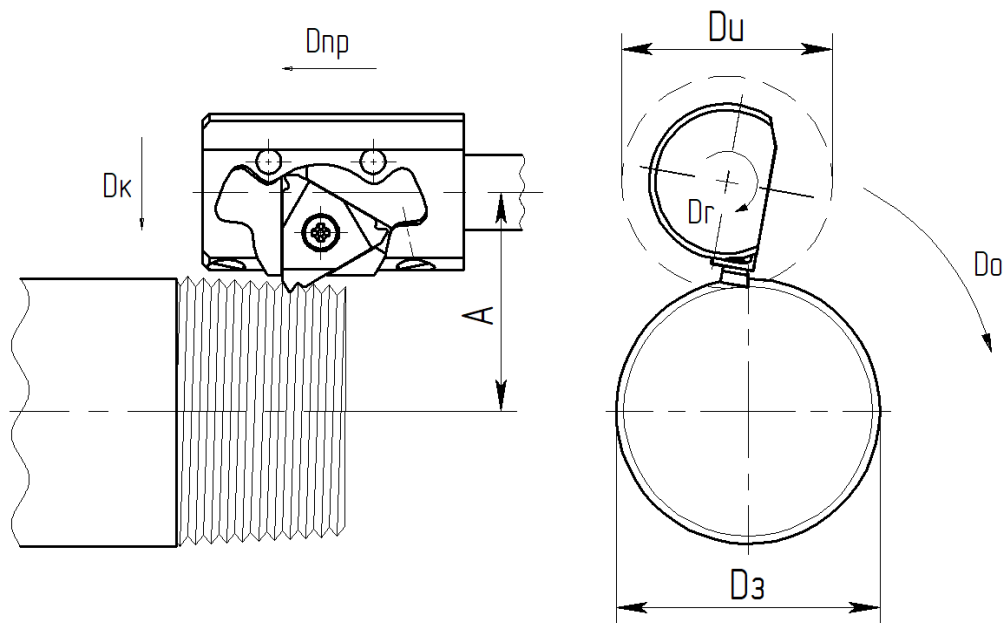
Схема обработки наружной резьбы по способу планетарного резьбофрезерования
